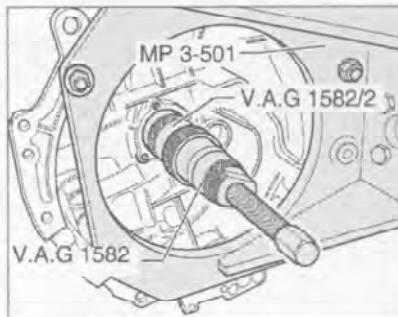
Выпрессуйте шарикоподшипник входного/первичного вала из картера сцепления.
